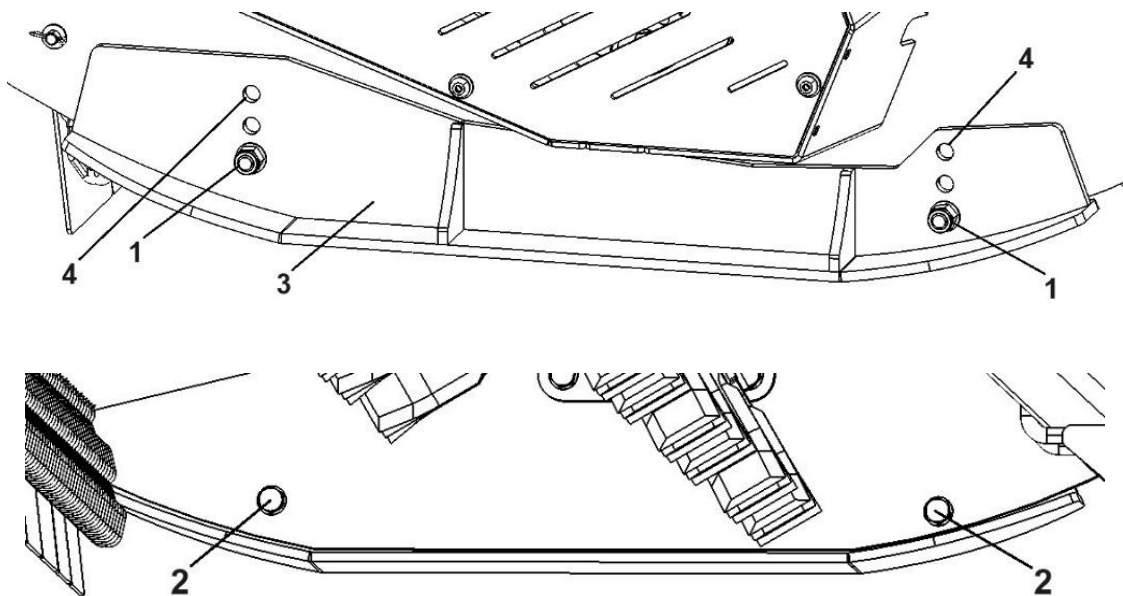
Einstellung der Position der seitlichen Kufen: 1 – Befestigungsmuttern, 2 – Befestigungsschrauben, 3 – Kufe, 4 – Einstellbohrungen
